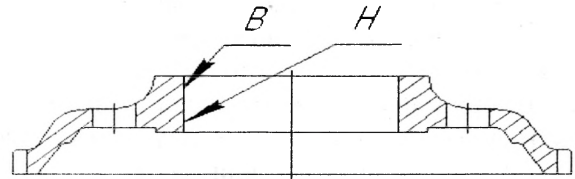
Условные обозначения мест расположения контролируемых параметров в детали: В — условно обозначенный «верх» детали; Н — условно обозначенный «низ» детали
